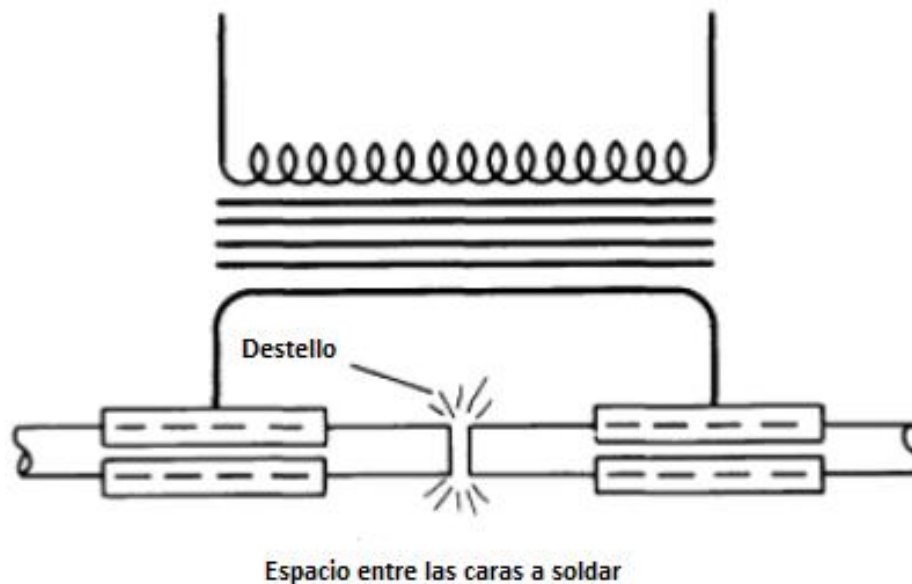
Ajuste típico de la soldadura a tope por destello con una separación entre las caras de dos barras a soldar.
